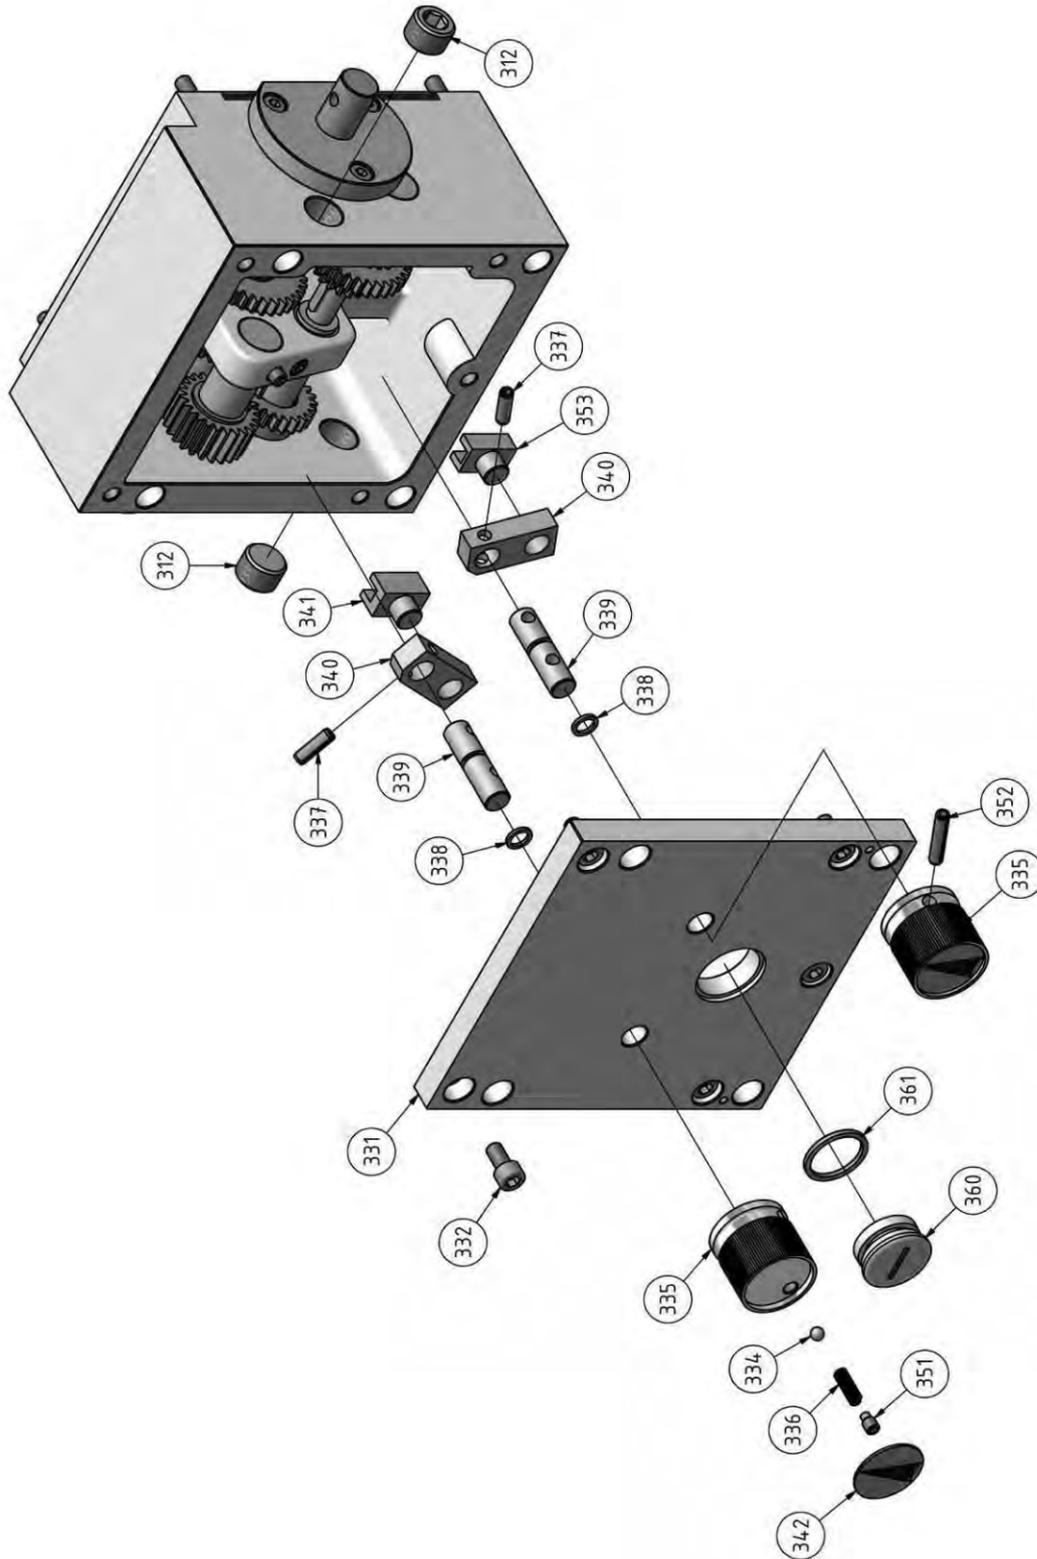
Vorschubgetriebe 1 von 2 - Engranaje de avance 1 de 2 - TU 2506
